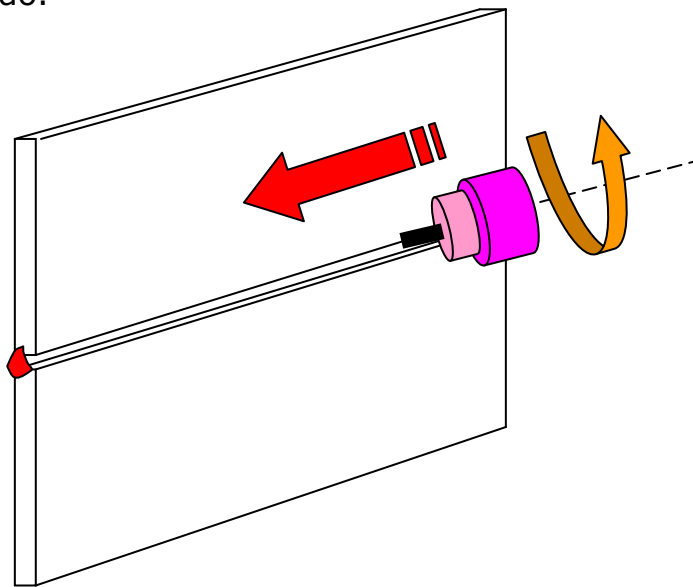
Realización de la soldadura de placas a tope con ranura cuadrada, en posición horizontal.
